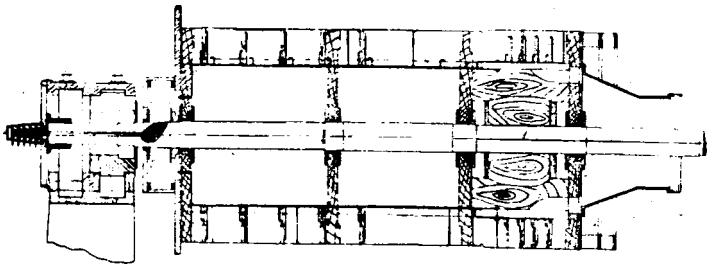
Схема расположения трубочек для замера давлений и скоростей воздуха по каналам ротора
